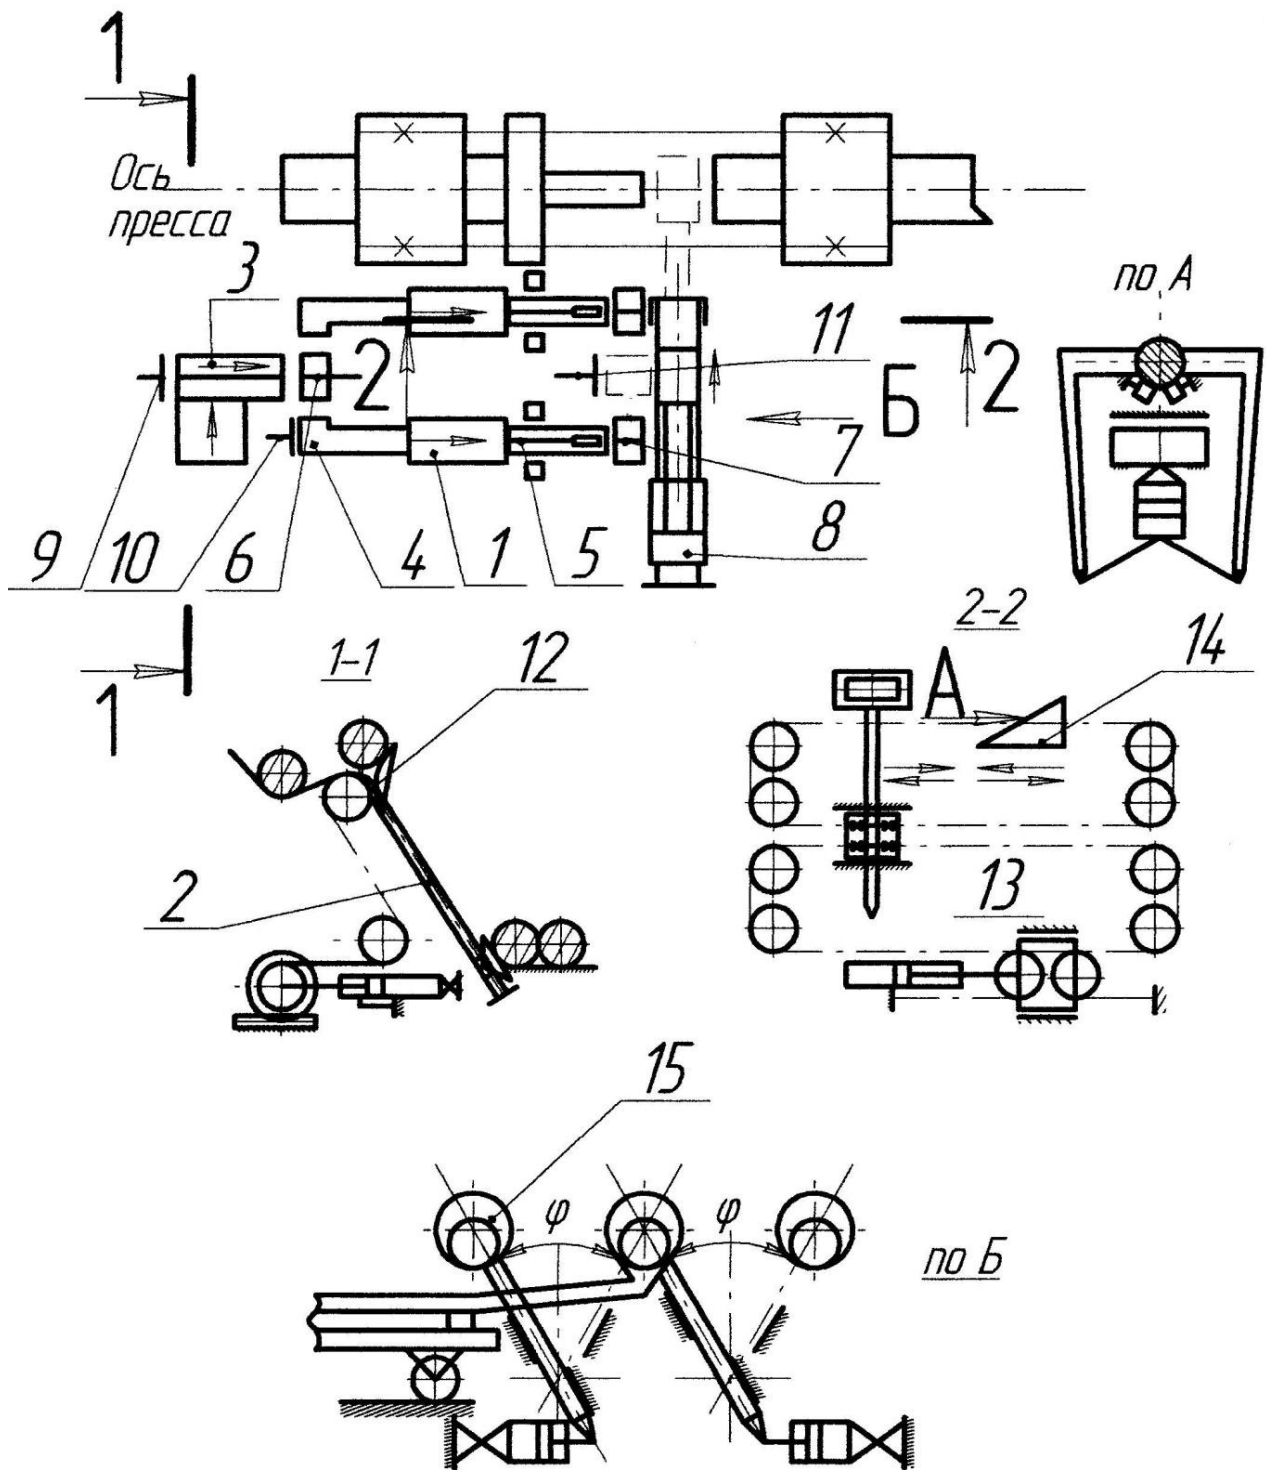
Схема подачі заготовок на вісь пресування
